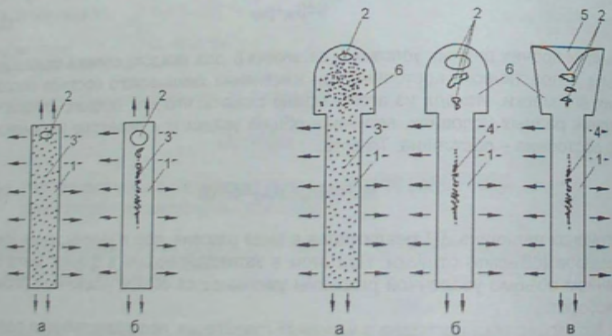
Схемы расположения усадочных дефектов в отливках, затвердевших в условиях всестороннего, равномерного теплоотода от отливки: 1 – отливка; 2 – усадочная раковина закрытого типа; 3 – пористость
